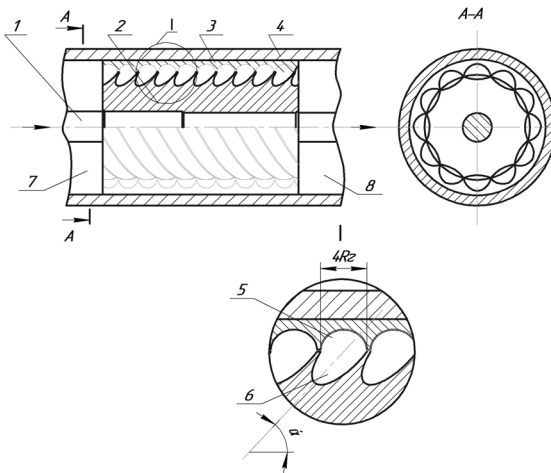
Удосконалені робочі органи насоса [8]: 1 – привідний вал; 2 – гвинт; 3 – втулка; 4 – корпус; 5 – гвинтова канавка напівкруглої форми; 6 – гвинтова канавка довгастої форми; 7 – камера підводу; 8 – камера відводу.
